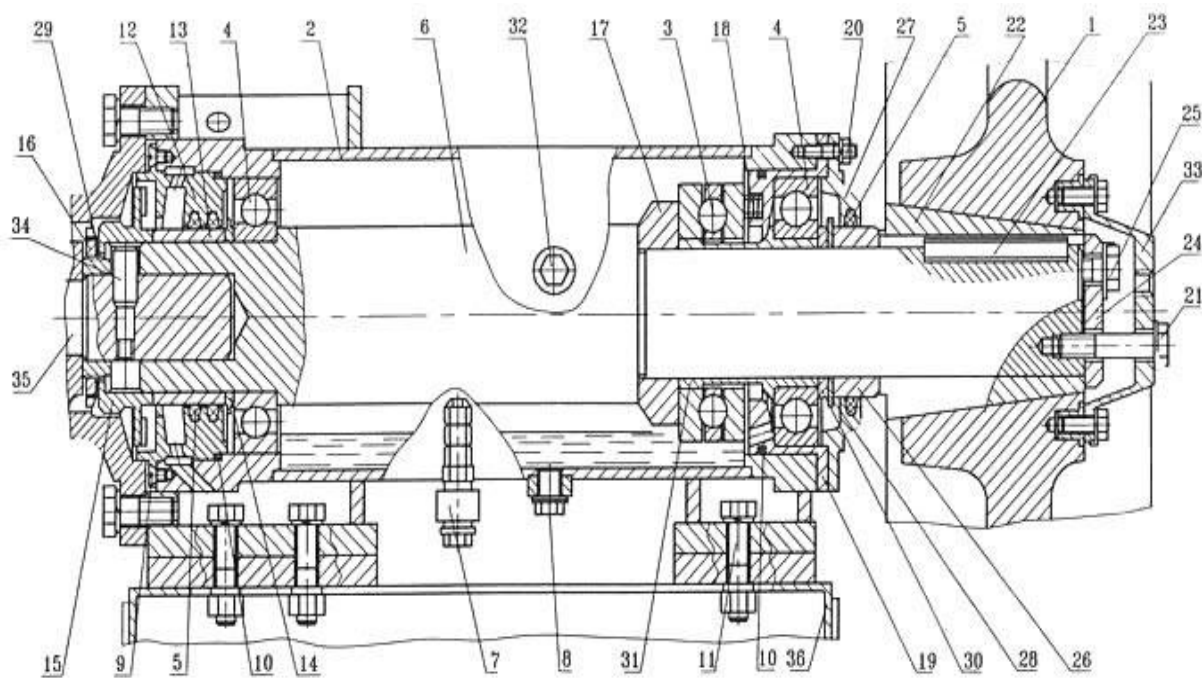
Схема устройства пресс-экструдера ПЭ - КМЗ
